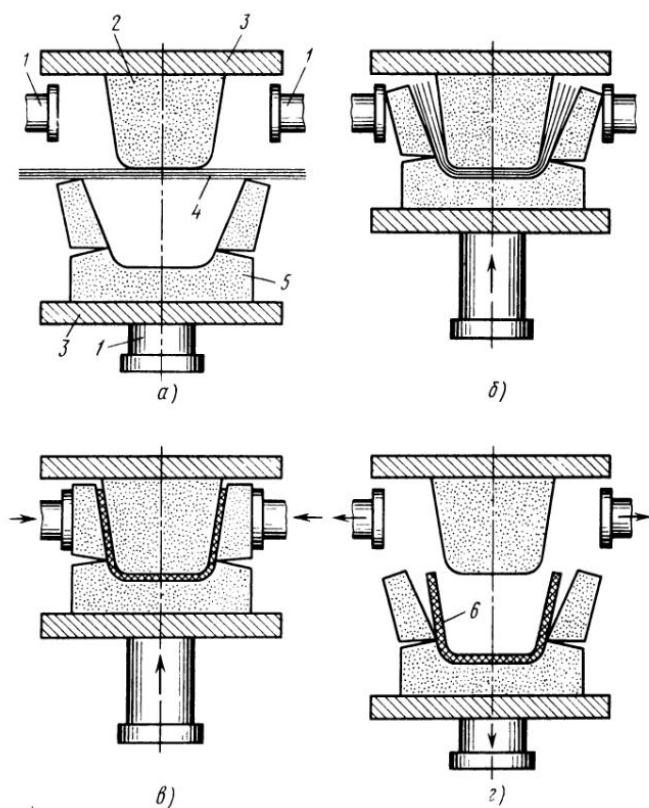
Схема и последовательность (а — г) работы пресса для изготовления заготовок глубокого профиля:
